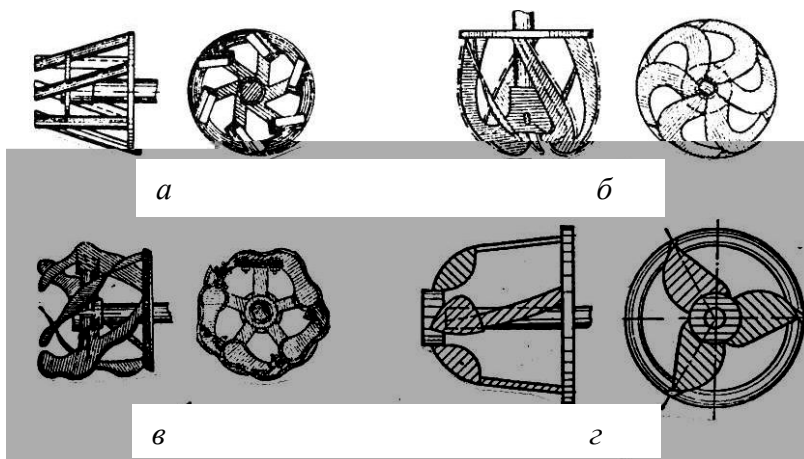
Фрезы наиболее типичных конструкций: а – открытая с плоскими ножами; б – закрытая (митрообразная) с ножами двойной кривизны; в – полукрытая с ножами волнообразной формы; г – отвально-режущими лопастями.
